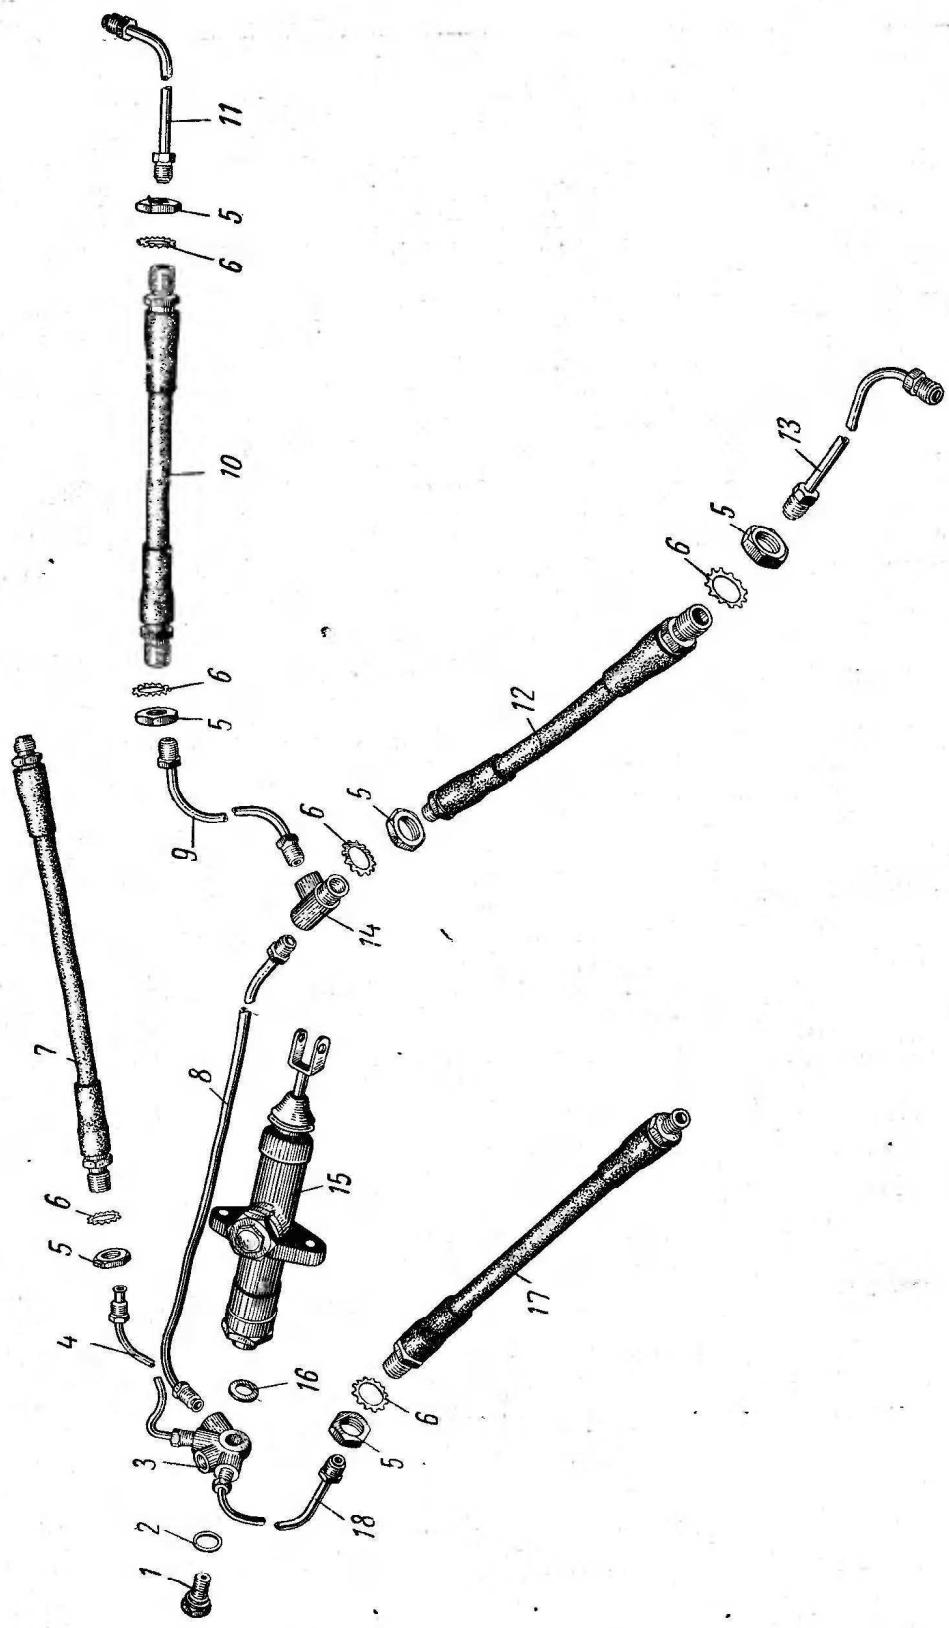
Rohrleitungen der hydraulischen Bremsbetätigung
